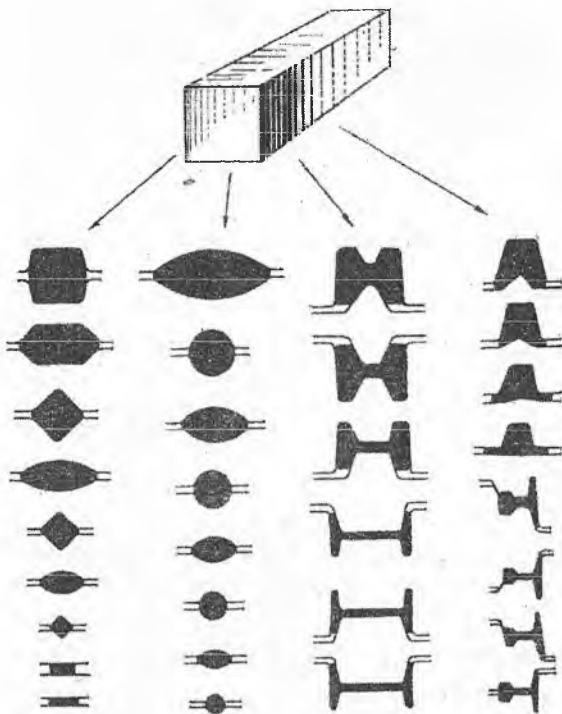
Так валки сортопрокатного стана превращают квадратную заготовку в полосу, пруток, двутавровую балку и рельс
